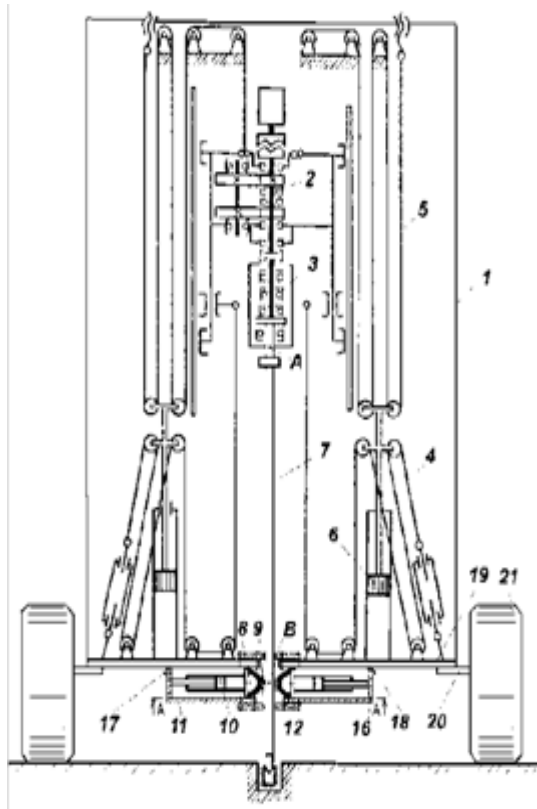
Схема бурового станка с НСП: 1 – мачта; 2 – редуктор; 3 – опорный узел; 4 – механизм подачи; 5 – канат подъема; 6 – гидроцилиндр напора; 7 – буровой став; 8 – НСП; 9 – зазор; 10 – гидроцилиндр; 11 – корпус устройства; 12 – фартук от попадания шлама; 16, 17 – стойки; 18 – основа мачты; 19 – рама станка; 20 – ось механизма передвижения; 21 – гусеница
